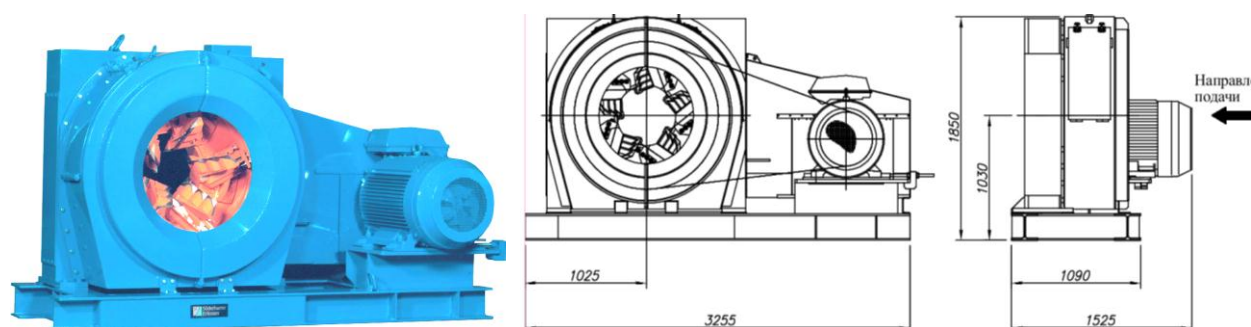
Станок для оцилиндровки бревен CamTrim:
